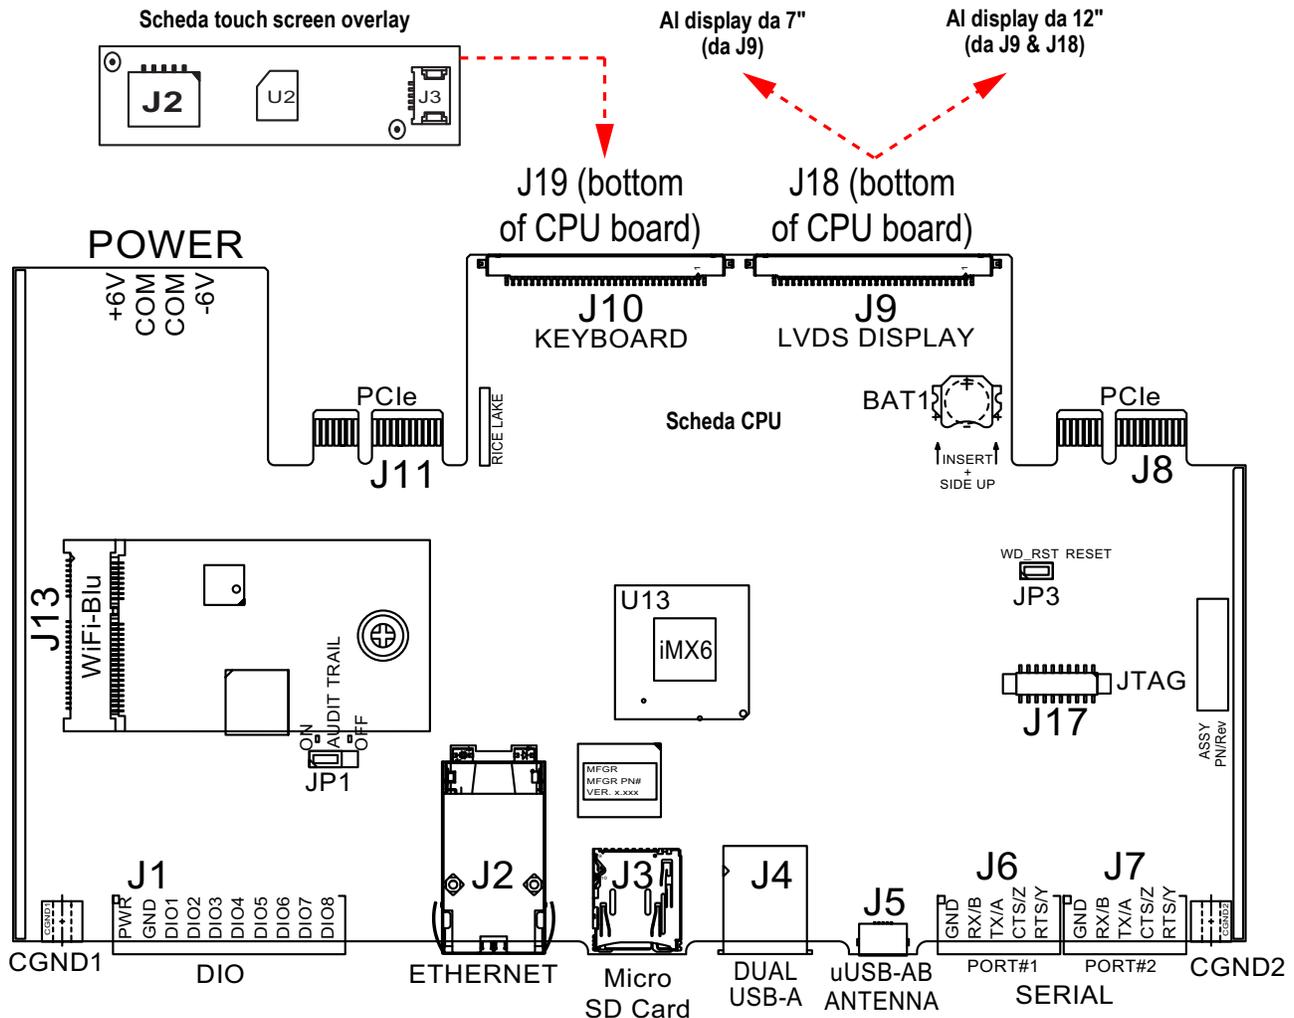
Versioni con montaggio a pannello – da 7" e 12" solo touch
